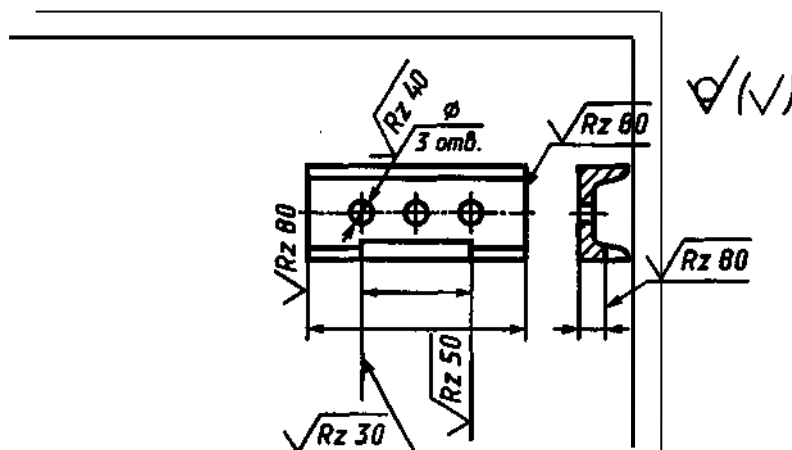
Пример обозначения шероховатости на чертеже
